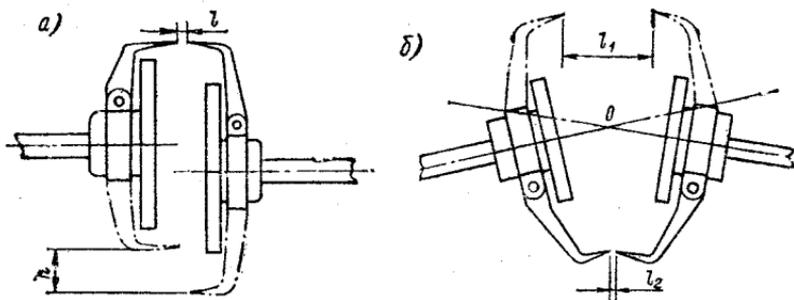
Определение неточности установки гребного вала: а — смещение осей; б — излом линии вала.
